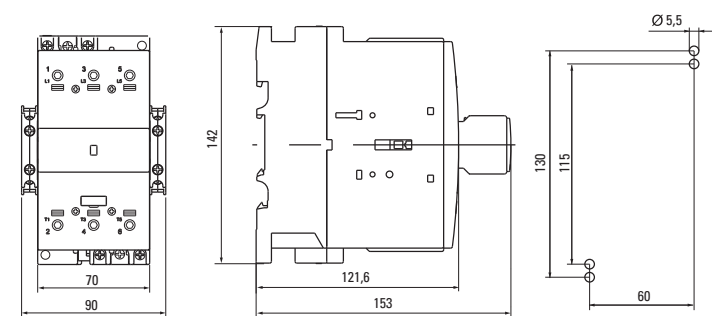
Габаритные и установочные размеры контакторов КМЗ 80А, КМЗ 90А, КМЗ 100А
